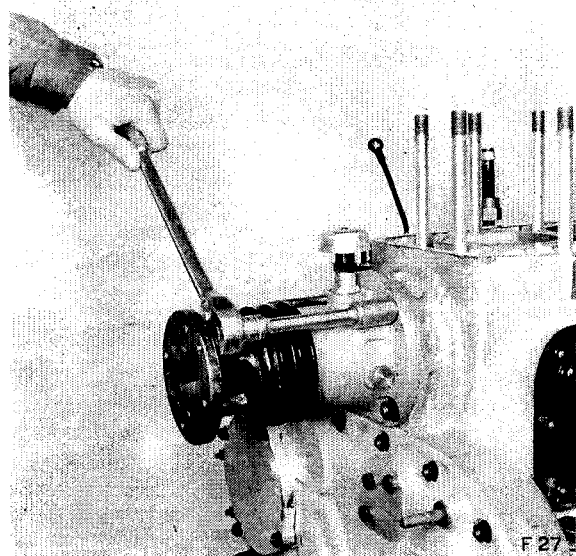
Lösen der Befestigungsschrauben für die Leckölleitung
